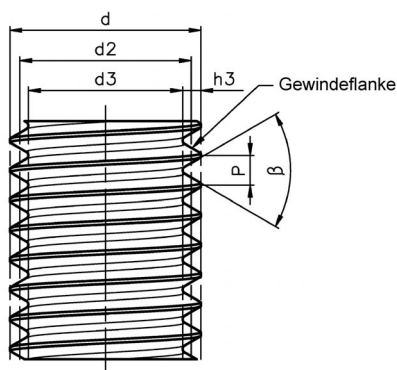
Bezeichnung eines Gewindes nach ISO (d = Außendurchmesser, d2 = mittlerer Flankendurchmesser, d3 = Kerndurchmesser, beta = Flankenwinkel, h3 = Gewindetiefe, P = Steigung).
